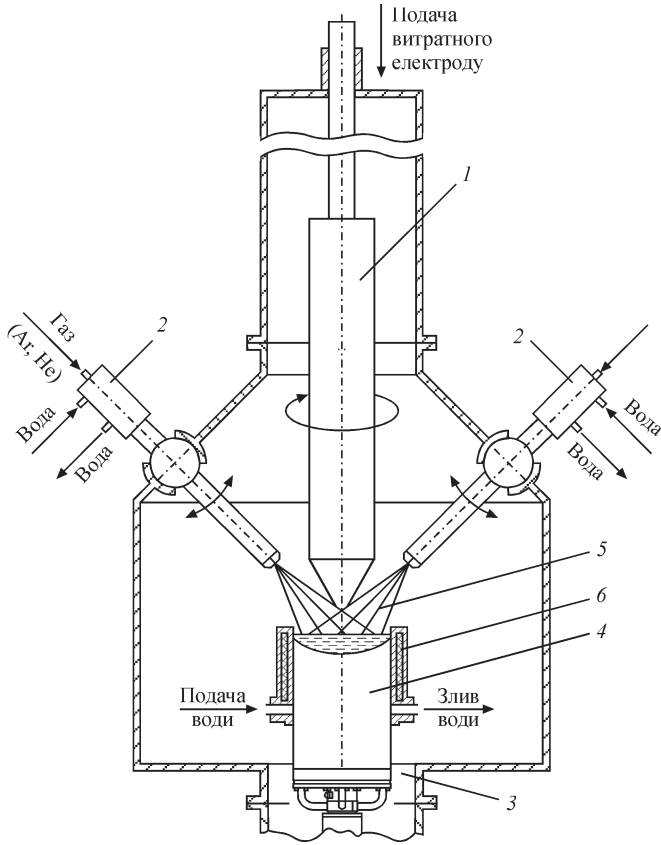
Схема плазмово-дугової печі: 1 — витратний електрод; 2 — плазмотрони; 3 — піддон; 4 — зливоч; 5 — плазма; 6 — кристалізатор
